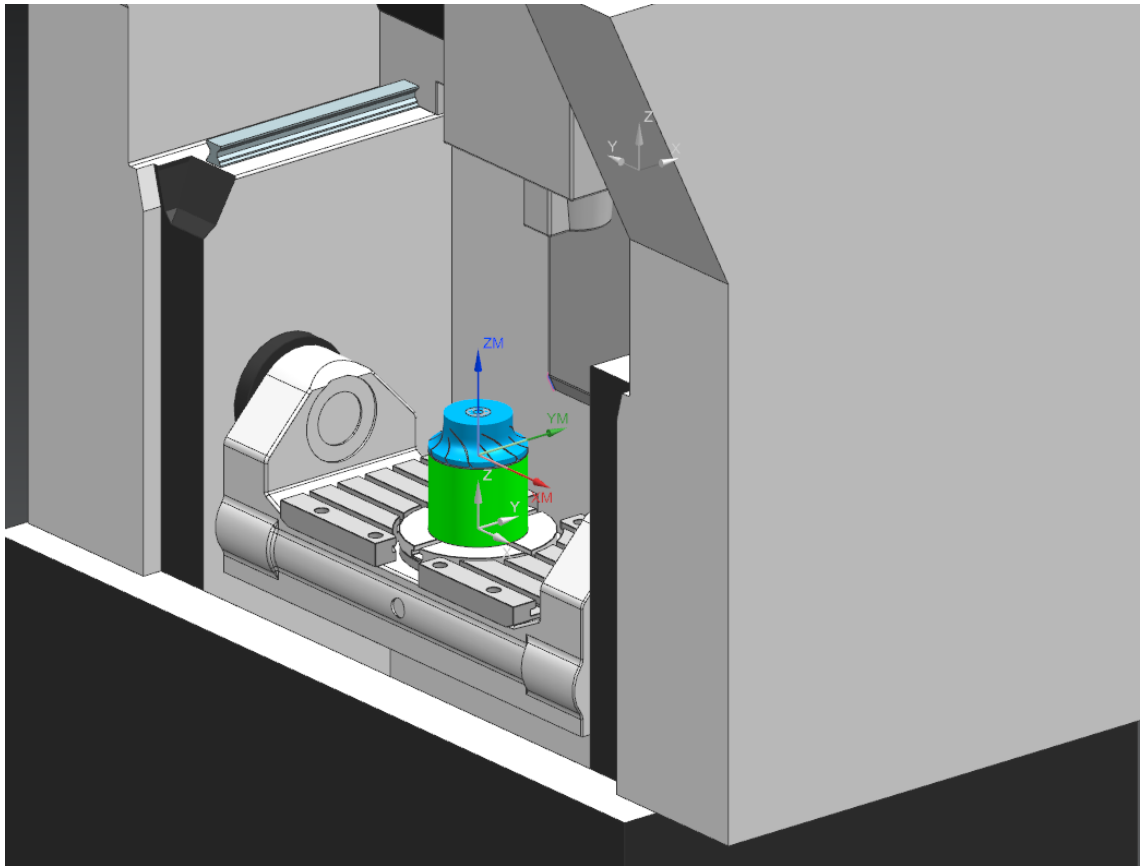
Montaje del material en bruto en la CNC 5 ejes.
